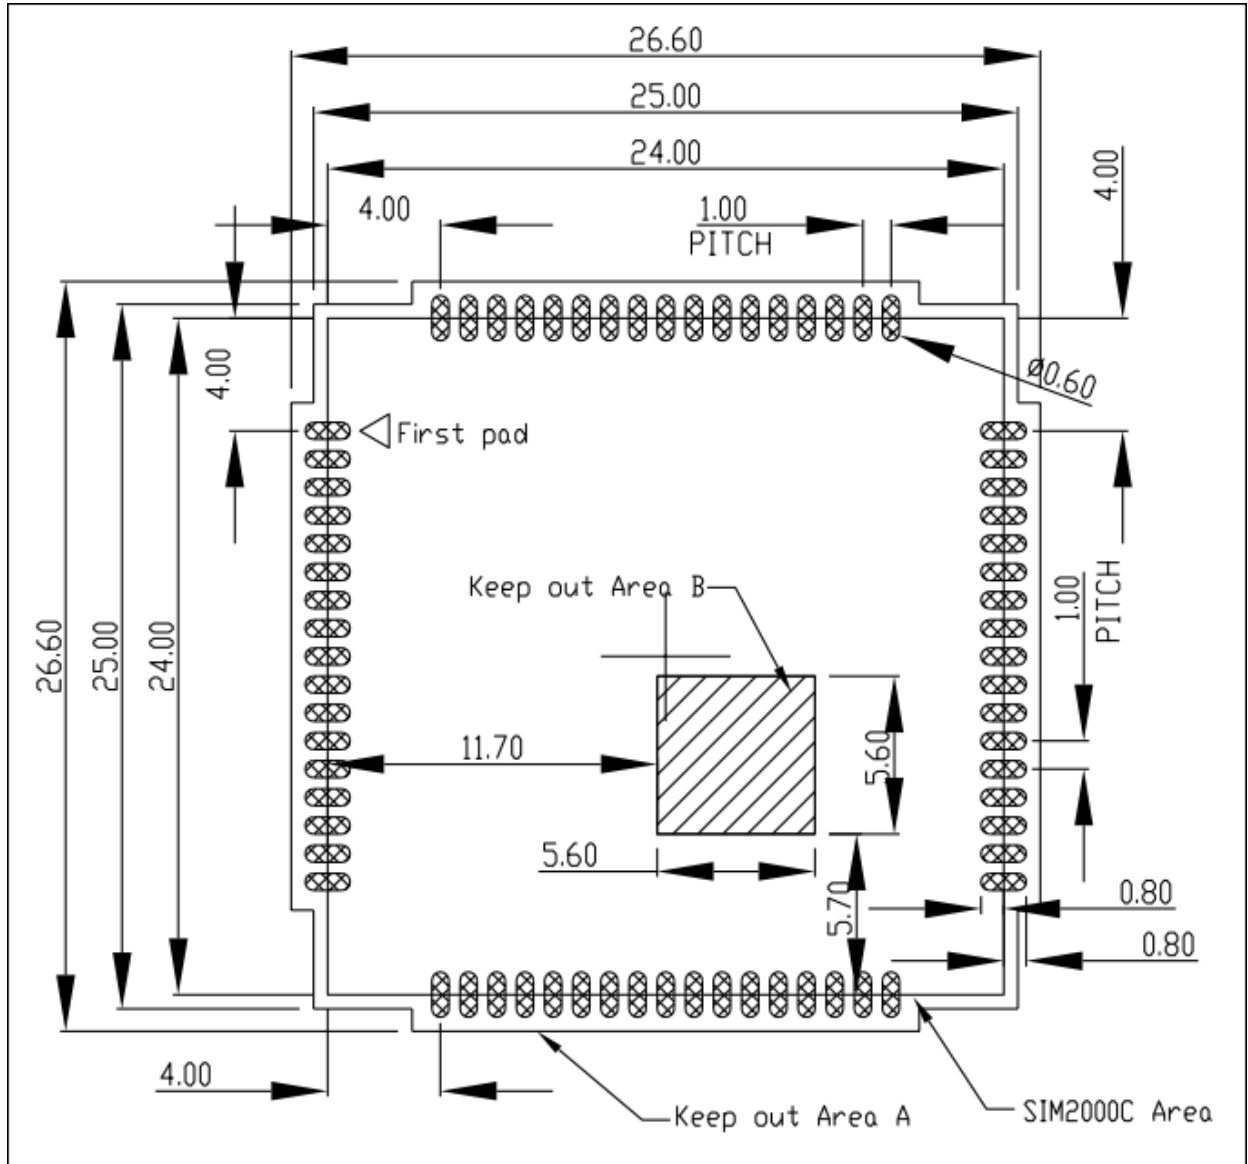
推荐 PCB 封装尺寸 (单位: 毫米)
